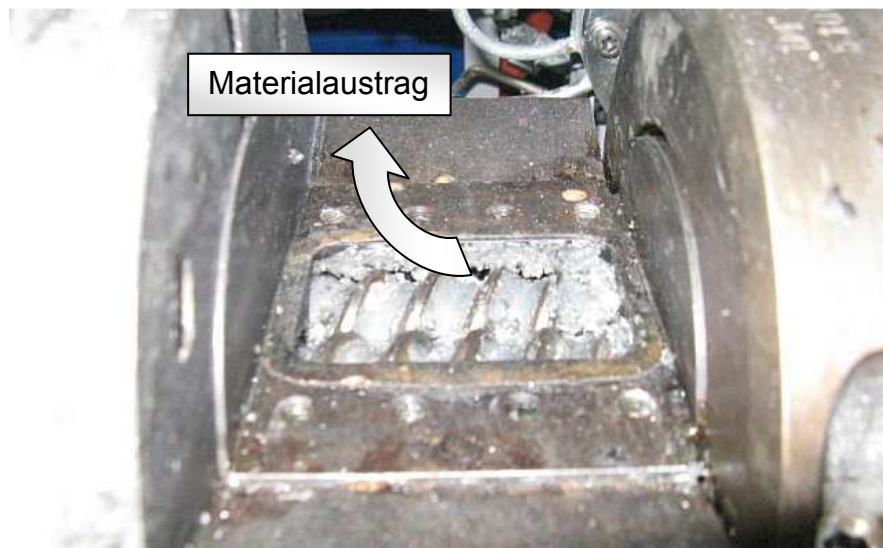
Geöffnetes Zylinderelement mit freier Sicht auf die Schnecken
